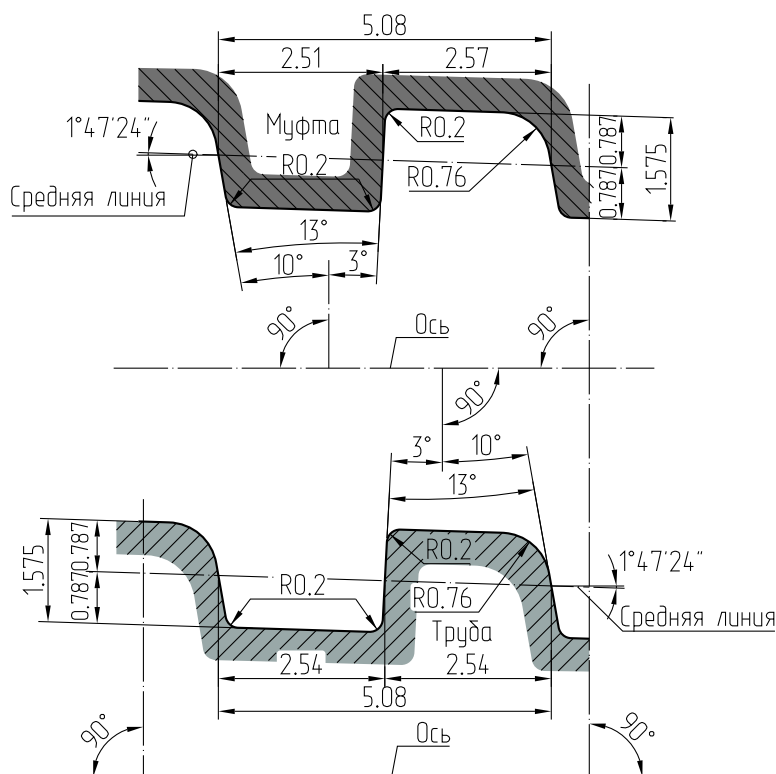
\*Вершины и впадины резьбы параллельны образующей конуса
